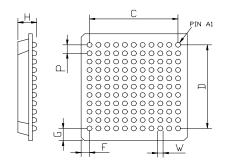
1.27mm PBGA 元件的焊盘尺寸
